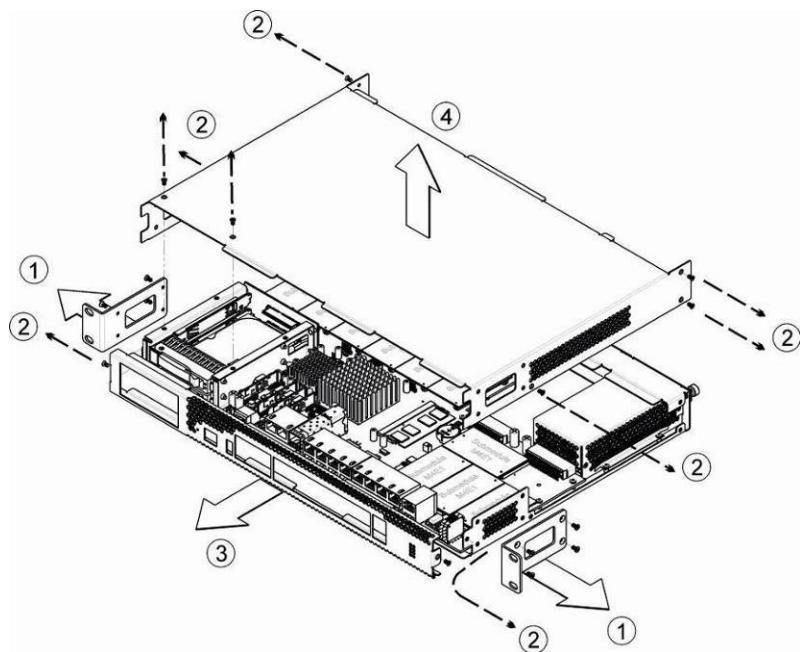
б – Порядок вскрытия корпуса SMG-2016
